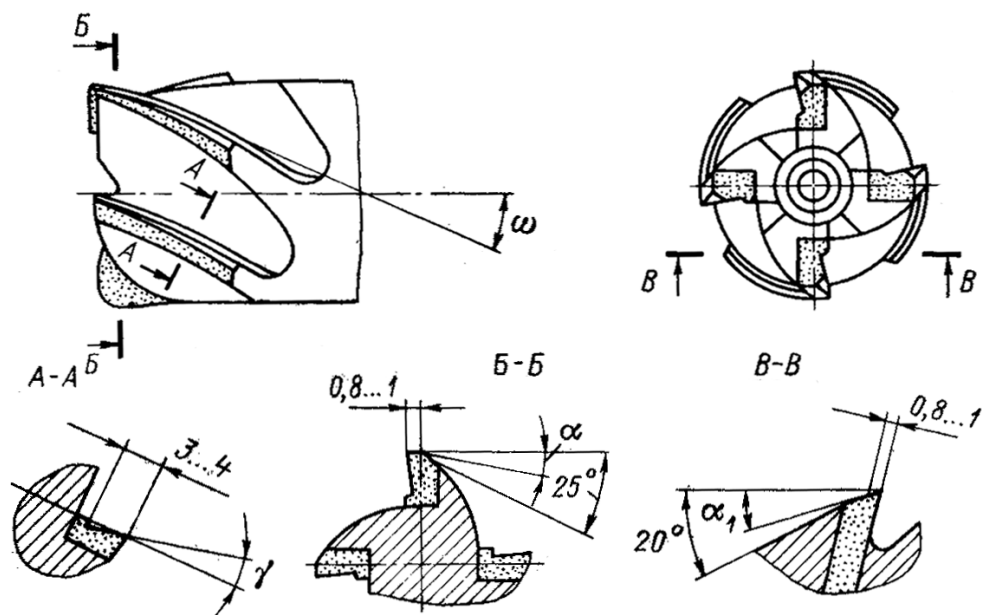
Типовая конструкция твердосплавной концевой фрезы
